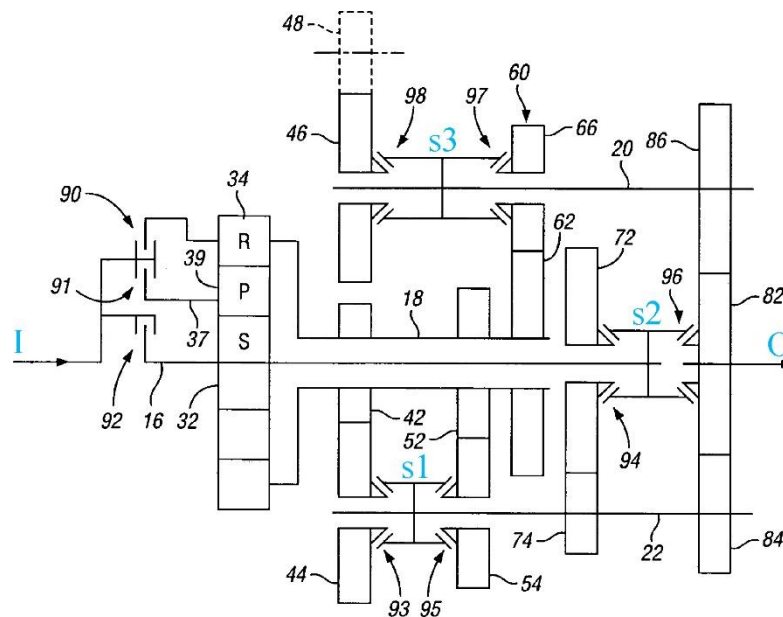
Кинематическая схема 9-ти ступенчатой вально-планетарной коробки передач.
